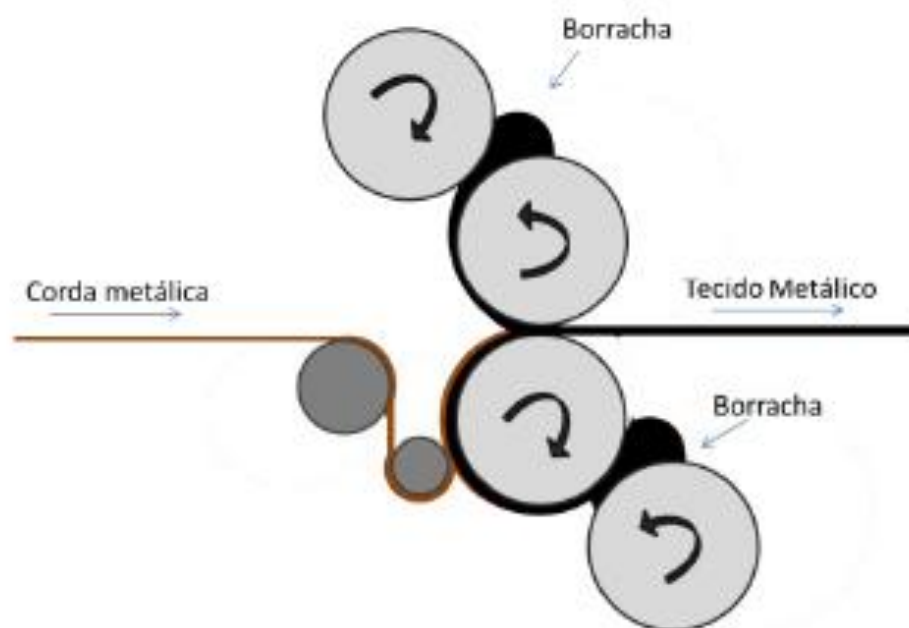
Representação do processo de calandragem do composto de borracha com componente de reforço
